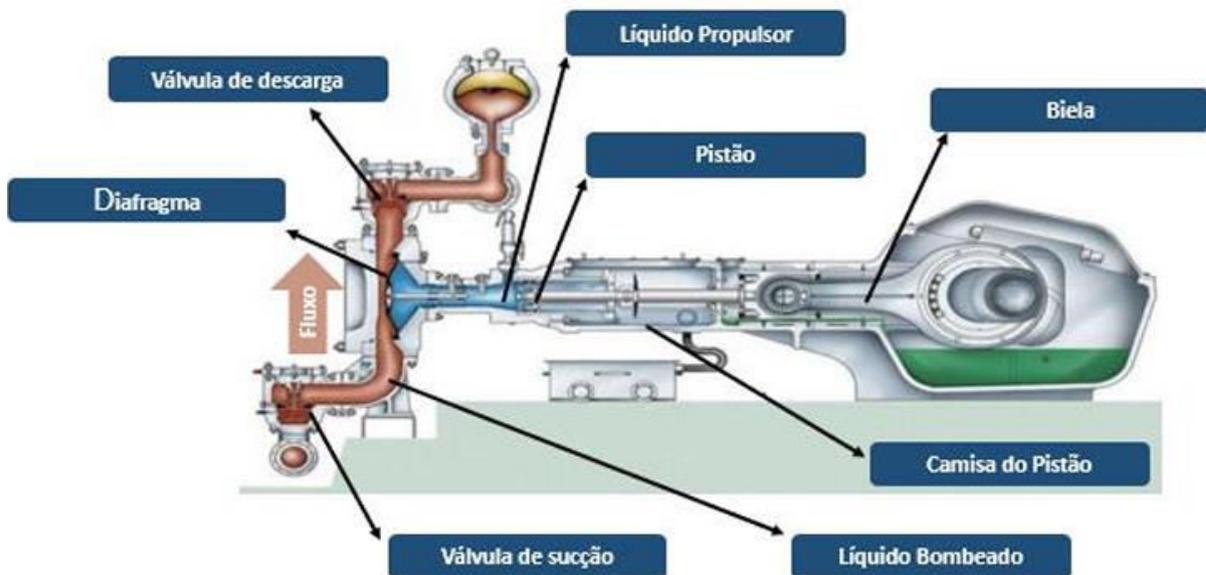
Desenho de um conjunto de uma bomba GEHO TZPM
